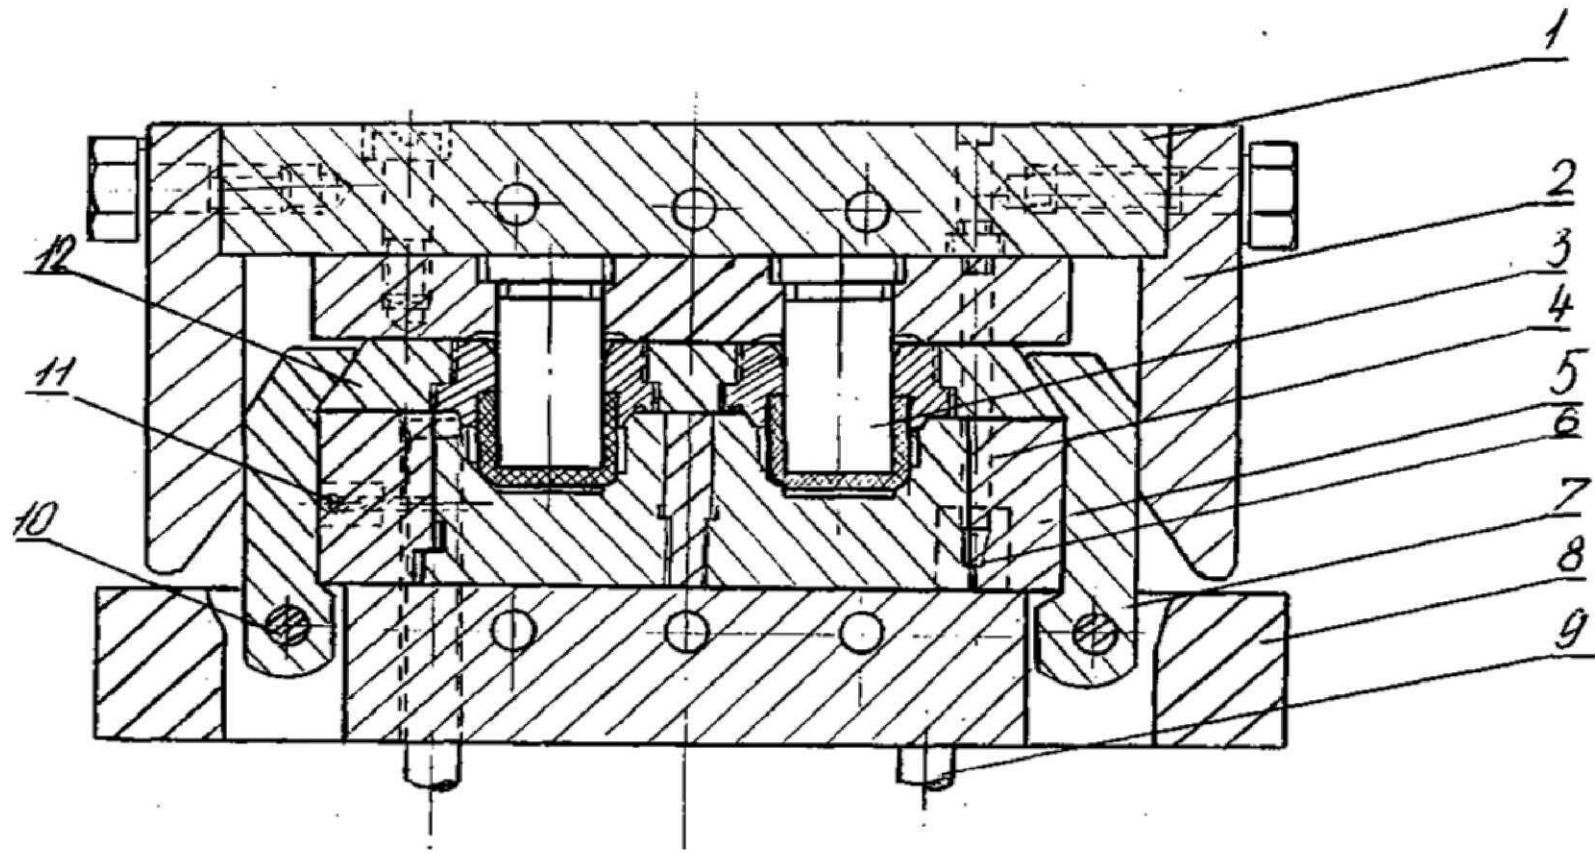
Пресс-форма для изготовления деталей методом прессования:
